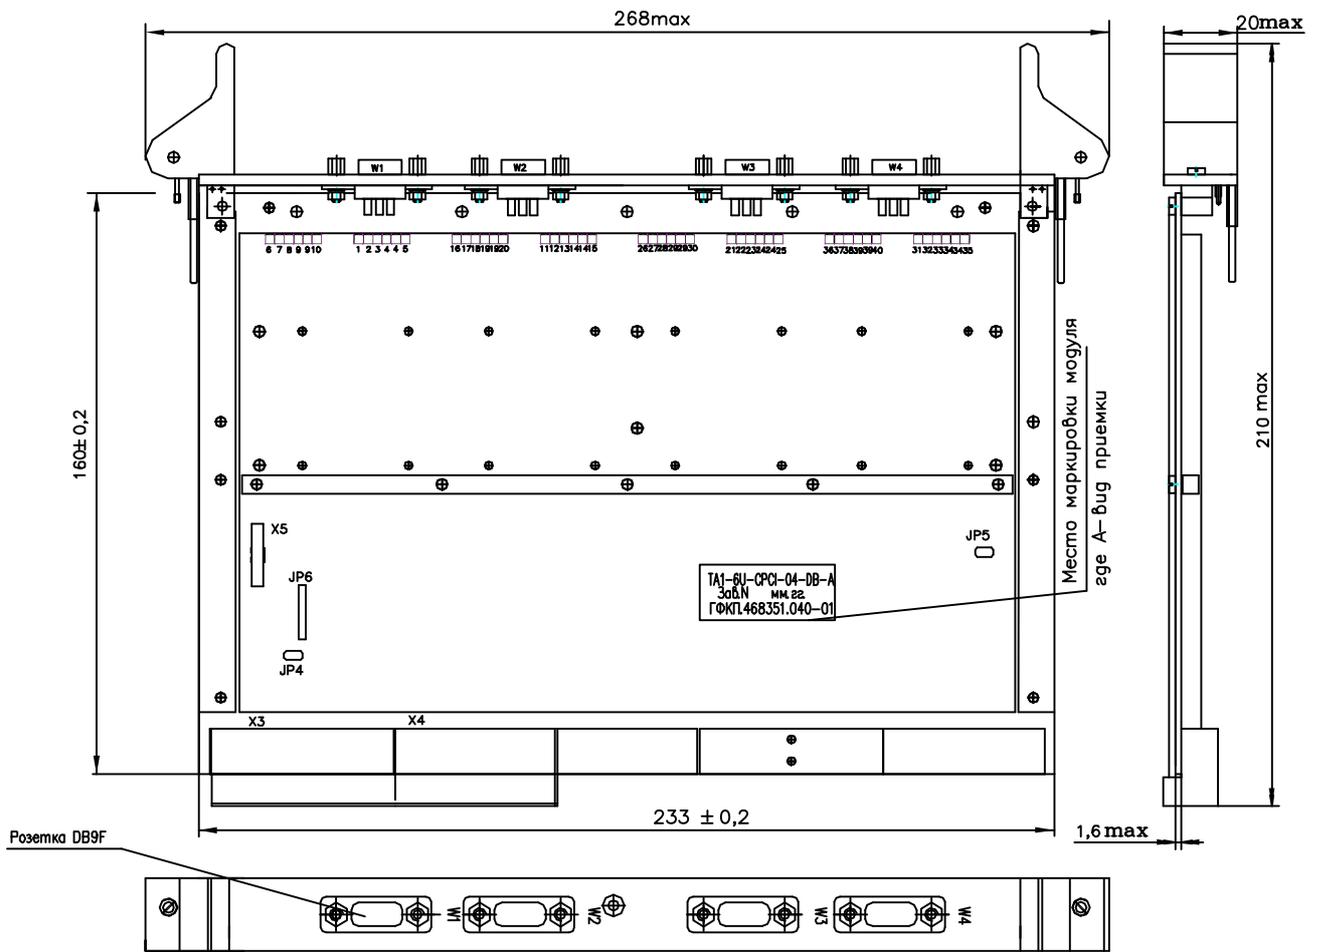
Габаритный чертеж изделия TA1-6U-CPCI-04-DB –А
